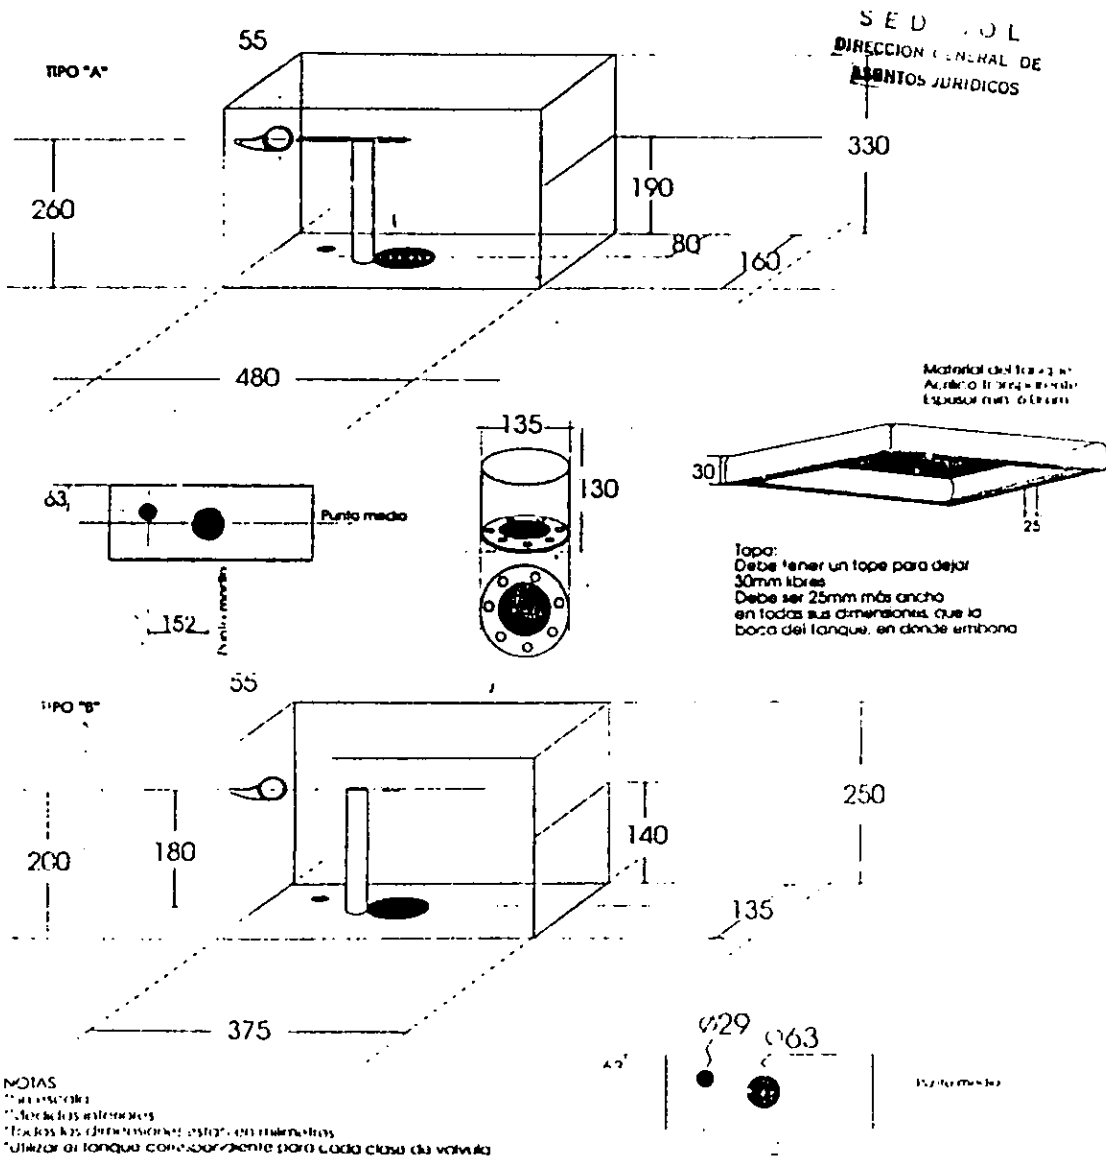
DIMENSIONES BASICAS DE TANQUES DE PRUEBA
